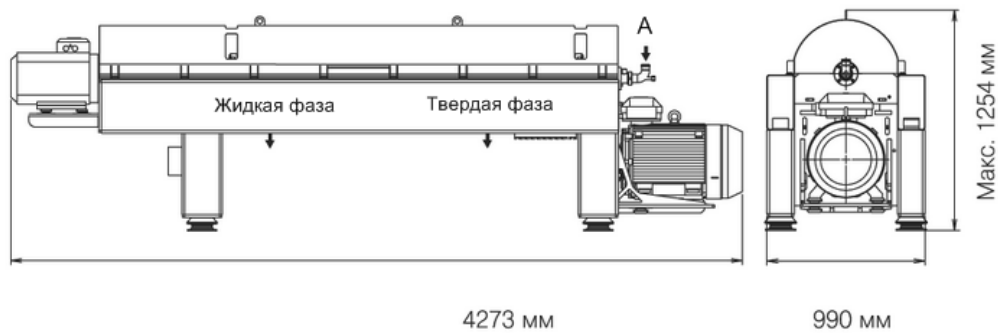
Габаритный чертеж декантера КРК70АМ001
